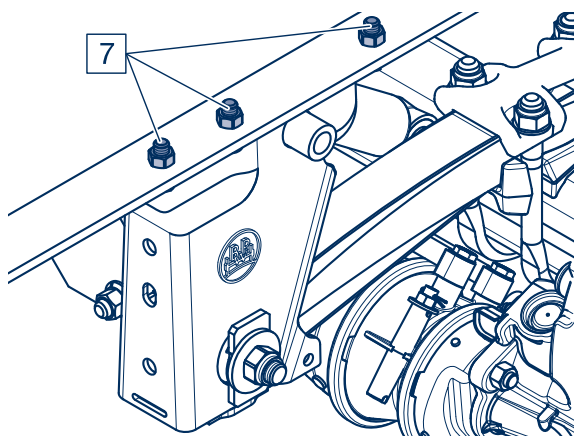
Резьбовое соединение опоры пневматической рессоры с продольным кронштейном
